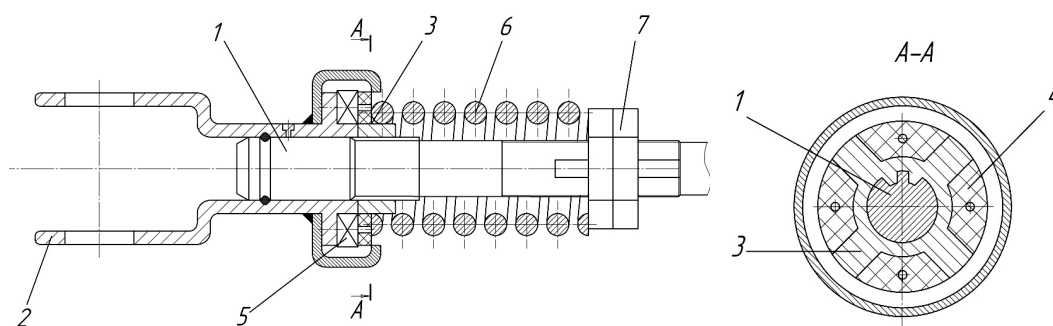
Предохранительное устройство: 1 — вал; 2 — вилка; 3 — втулка; 4 — упругий элемент; 5 — двухкулачковые шайбы; 6 — пружина; 7 — регулировочные гайки
